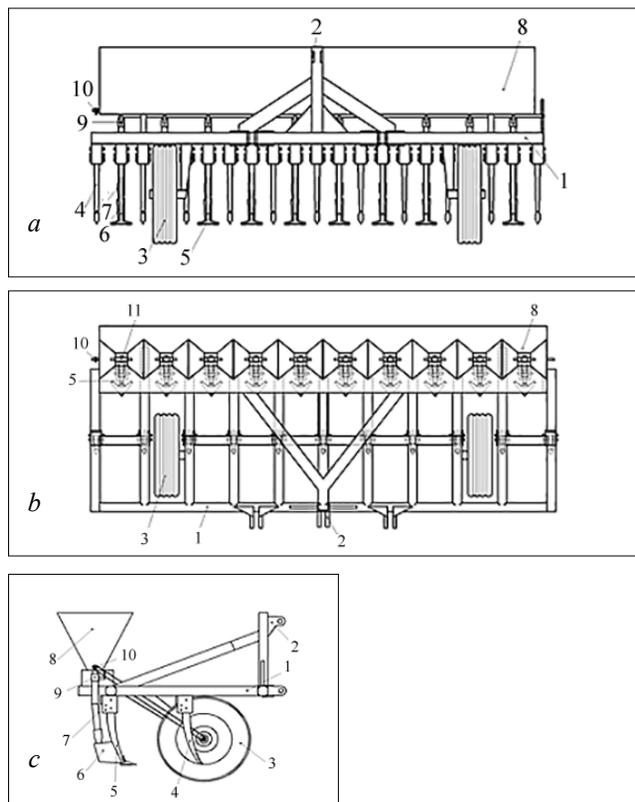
Схема агрегата для вынесения минеральных удобрений в ходе предпосевной обработки почвы: а – вид спереди; б – вид сверху; с – вид сбоку; 1 – рама агрегата; 2 – навеска рамы; 3 – опорное колесо; 4 – стойки с узкими рыхлительными лапами; 5 – стойки со стрельчатыми лапами; 6 – сошники для вынесения минеральных удобрений; 7 – трубопровод для минеральных удобрений; 8 – бункер; 9 – регулятор поступления минеральных удобрений; 10 – заслонка трубопровода; 11 – измельчитель
